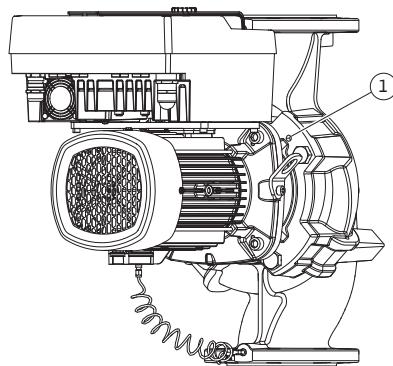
Издласкайте окомплектовката по резбовите на корпуса
